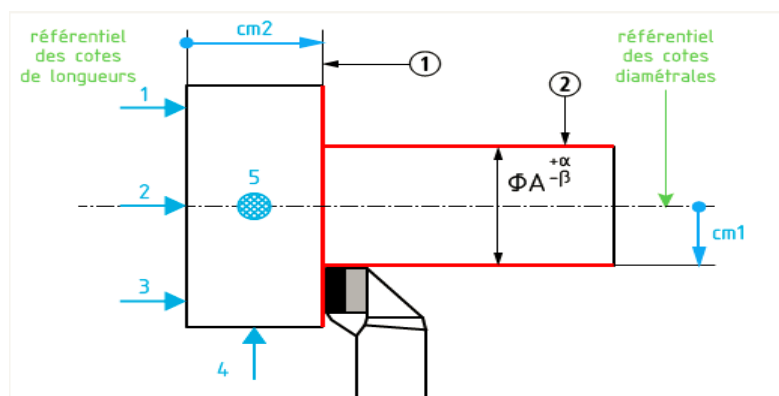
Indication des côtes machine réaliser sur un tour.
